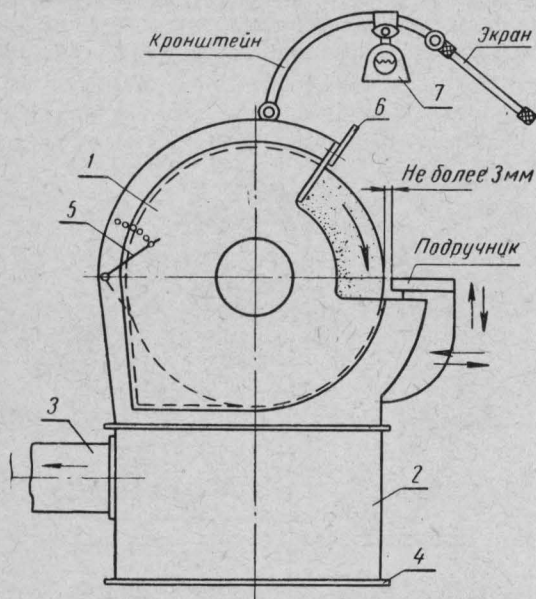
Схема предохранительных устройств для обдирочно-заточного станка:
